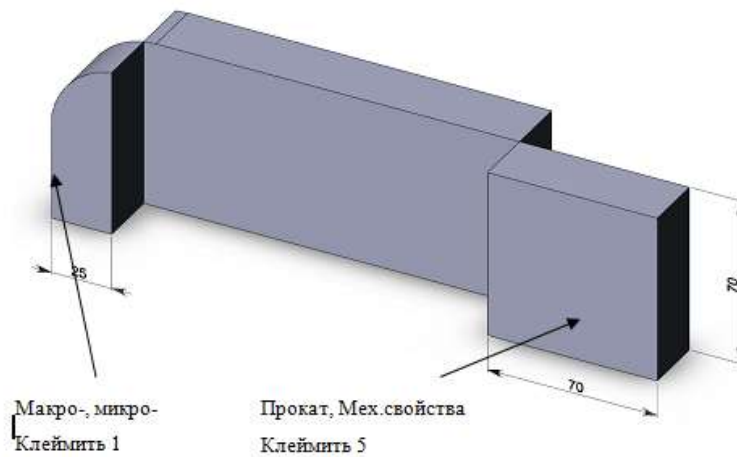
Схема раскроя на образцы заготовки №1
